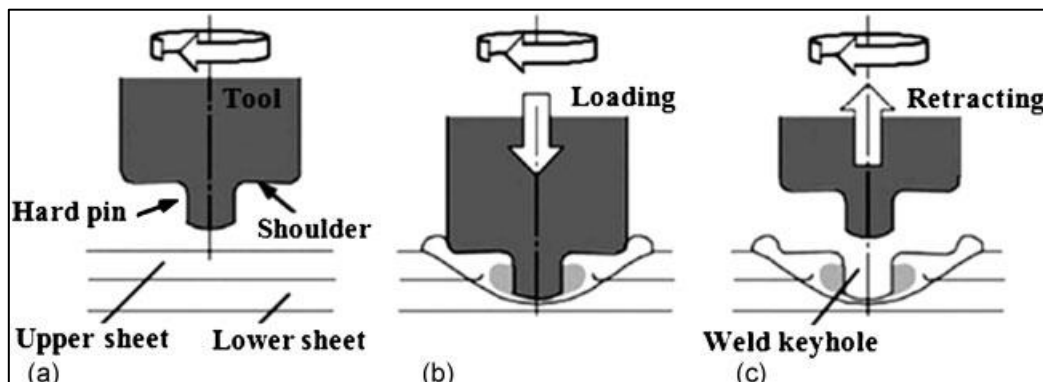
Esquema ilustrativo do processo Friction Stir Spot Welding [1].
